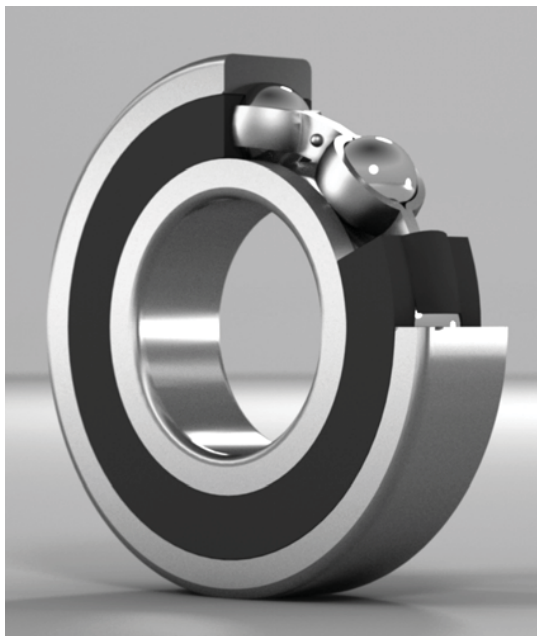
Подшипник с твердосмазочным наполнителем (АФЗ)
